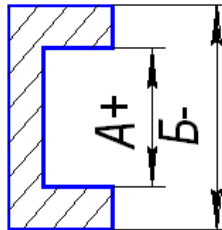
Схема для призначення «знака» допуска виливка
